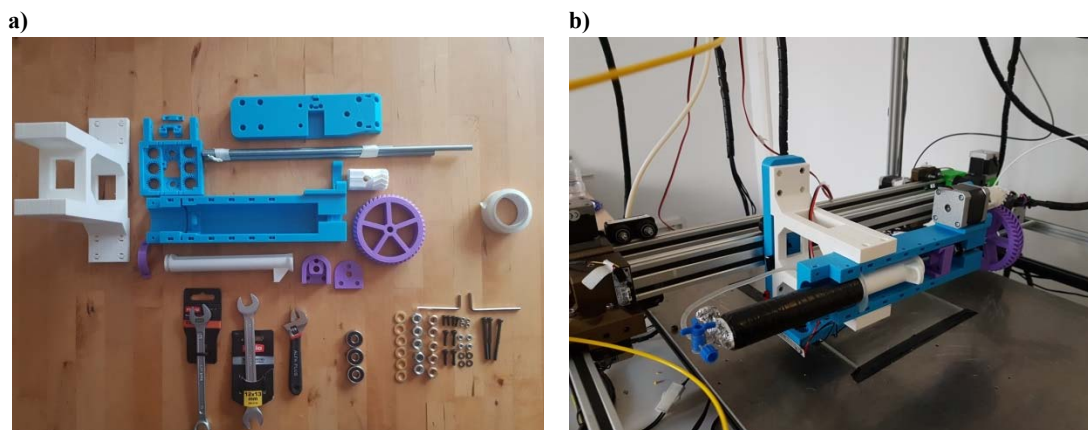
a) Peces que formen el capçal de deposició de líquid. b) Capçal ja muntat a la impressora 3D IQuEX . Font: [353].
